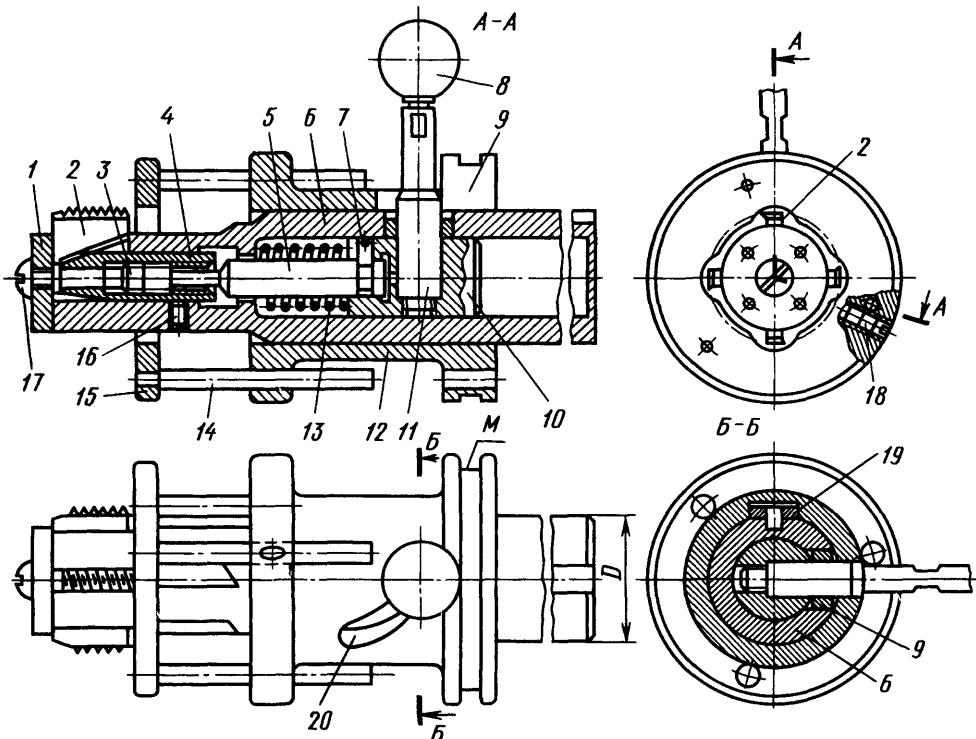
Невращающаяся винторезная головка для нарезания внутренней резьбы
